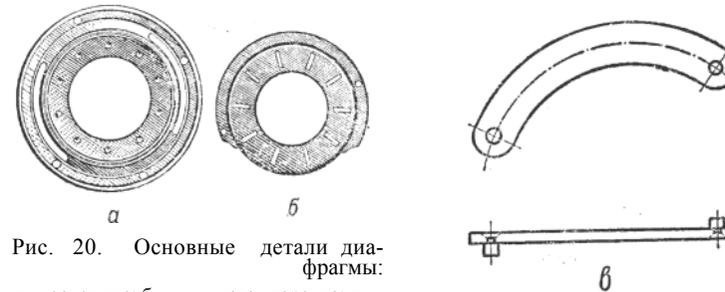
Основные детали диафрагмы: а — основные; б — шлицевал коронка; в — лепестки.
